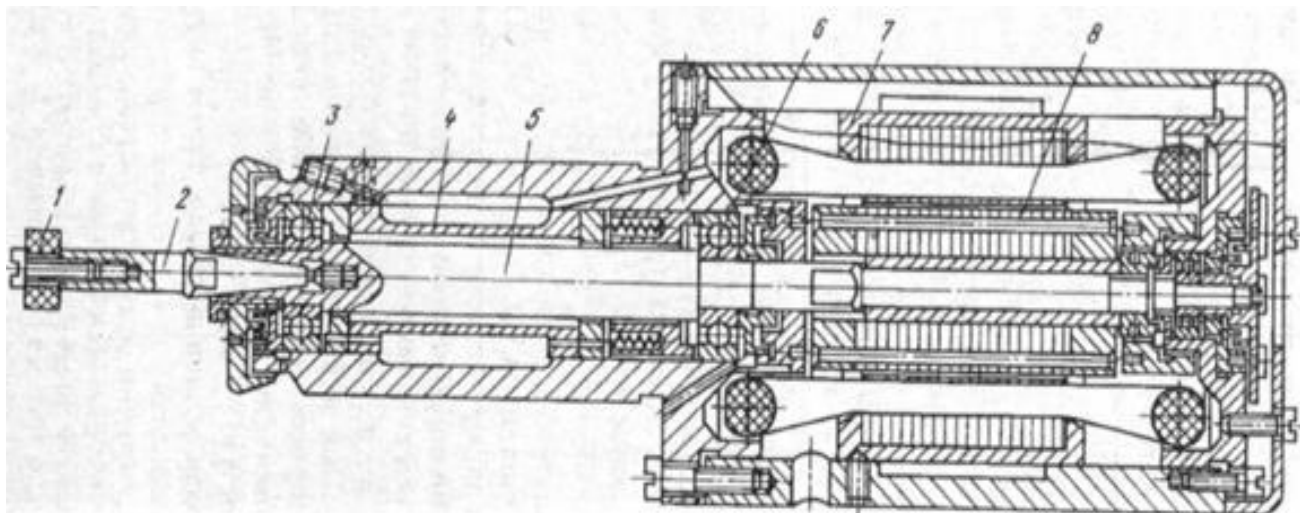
Электрошпиндель внутришлифовального станка: 1 - шлифовальный круг, 2 - оправка шлифовального круга, 3 - передняя опора шпинделя, 4 - гильза, 5 - шпиндель, 6 - задняя опора шпинделя, 7 - статор электродвигателя, 8 - ротор электродвигателя.
